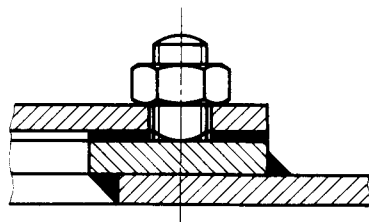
Goujon fileté soudé sur le cadre des trous de main
